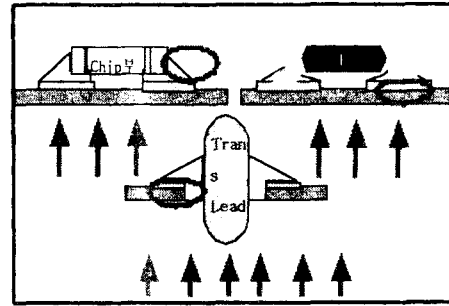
Sn-0.5Cu-0.1Ni Soldering시 부품의 결정립 조대화 기구
